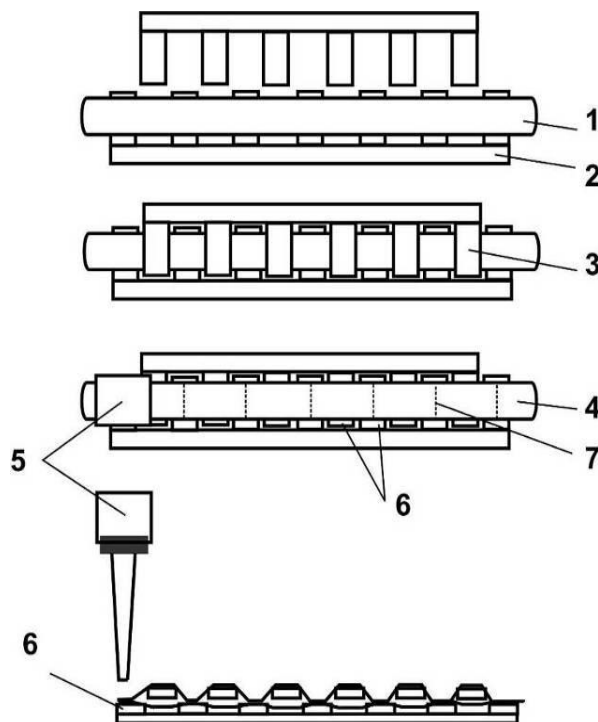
Схема способа изготовления и ультразвуковой сварки решёток
